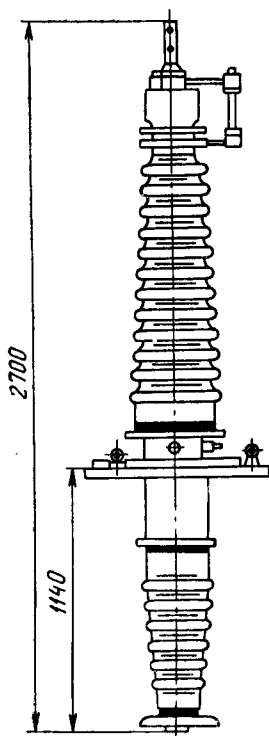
Малогабаритный конденсаторный ввод на 110 кВ типа МВ-110/600.
